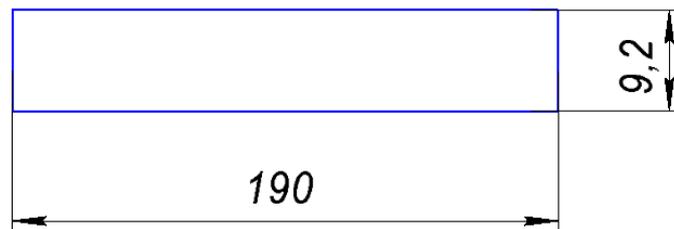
Эскиз поверхности, обработанной черновым фрезерованием
